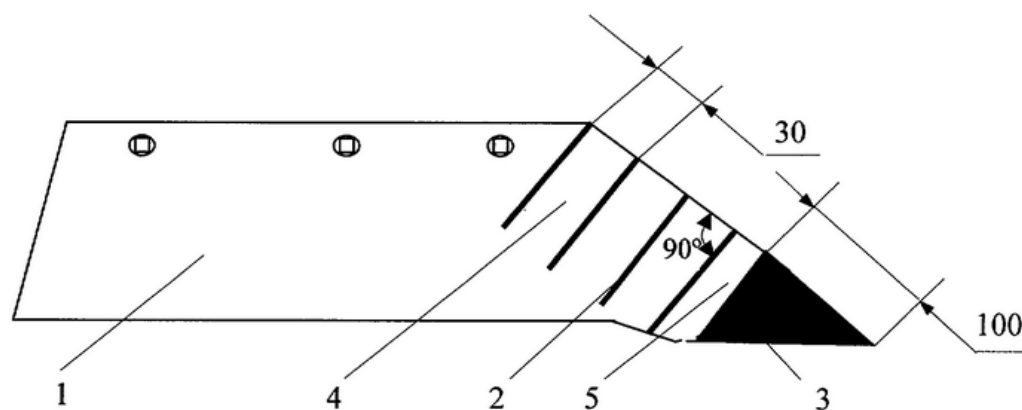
Лемех, армированный в области носка с наплавленной заглубляющей частью (1 - рабочая поверхность, 2 - армирующие валики, 3 - наплавленный металл, 4 - область образования лучевидного износа, 5 - заглубляющая часть)
